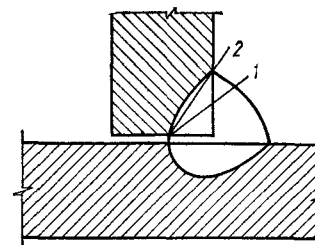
Схема расчетных сечений сварного соединения с угловым швом
